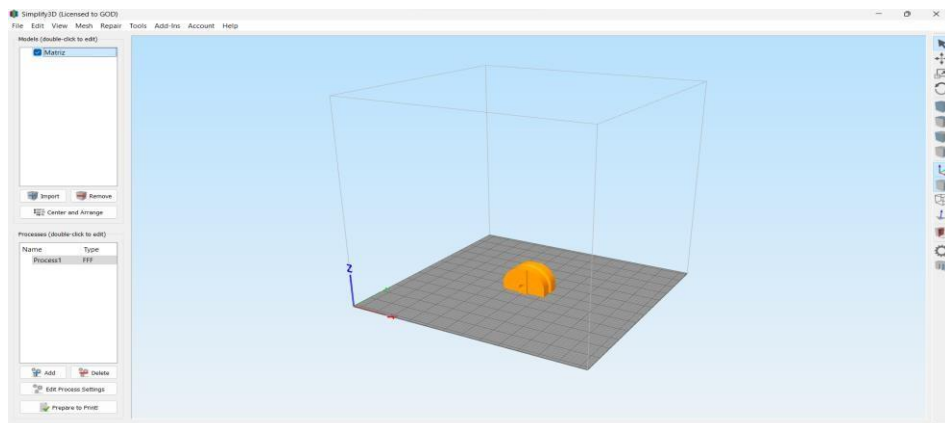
Desenho matriz de dobra com raio 30mm, para máquina CNC de dobra
